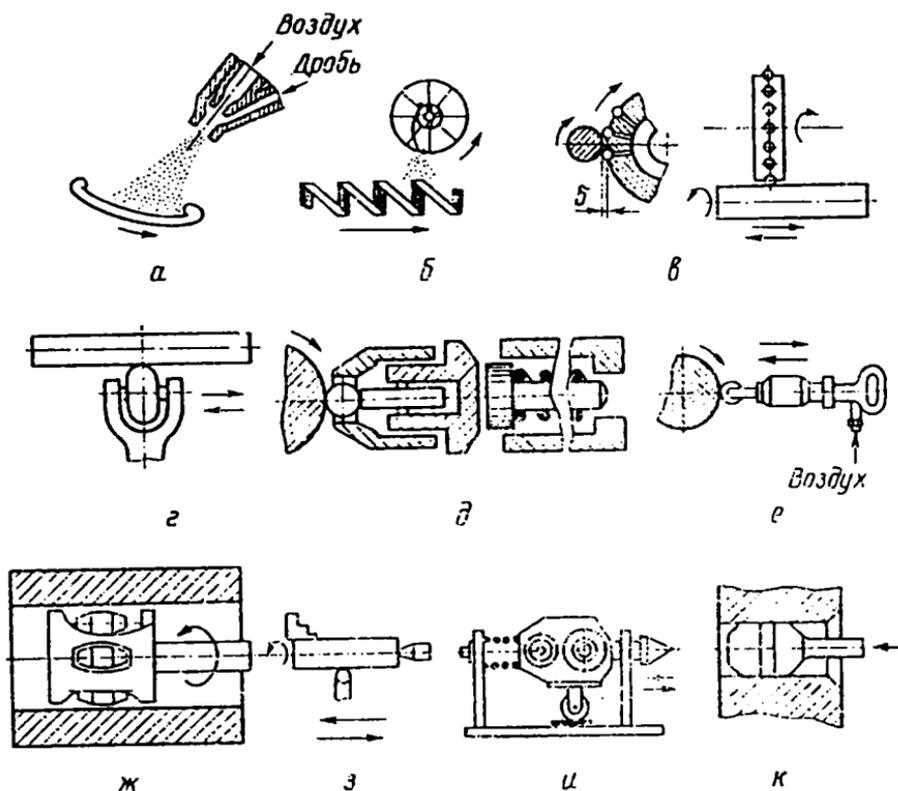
Схемы основных видов поверхностного пластического деформирования: а, б — дробеструйная обработка; в — центробежно-шариковый наклеп; г, д — обкатывание роликом и шаром, е — обкатывание вибрирующим роликом; ж — раскатывание отверстий роликом; з — алмазное выглаживание; и — чеканка; к — дорнование
